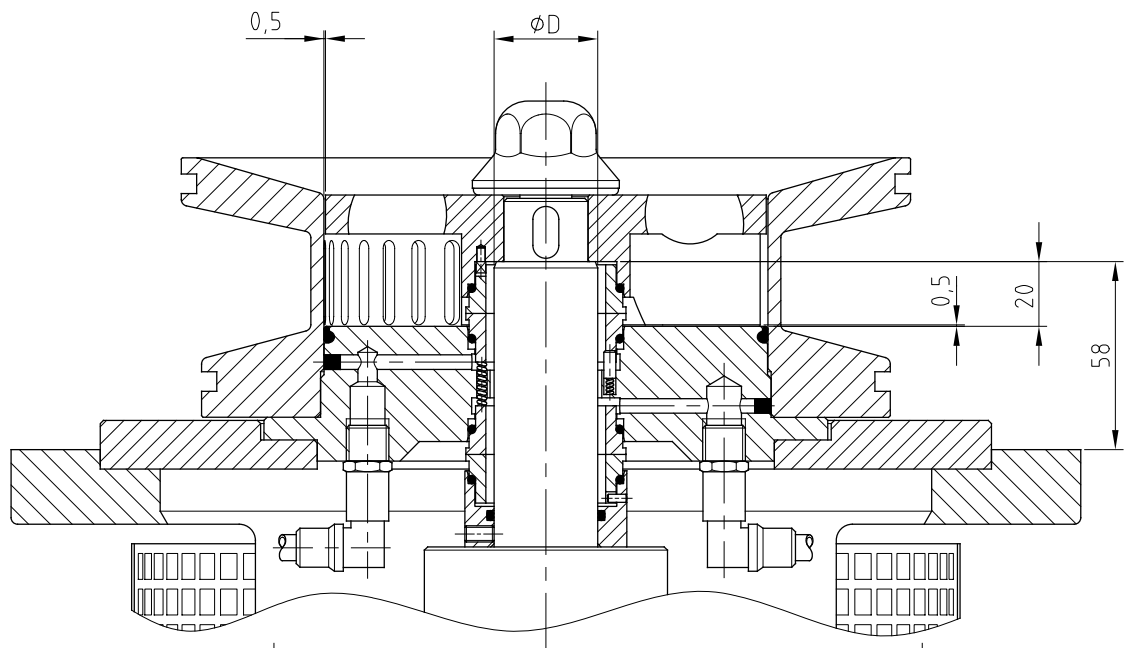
Детальный вид пружин позиционеров для размера ME-6125/6130 RE.
